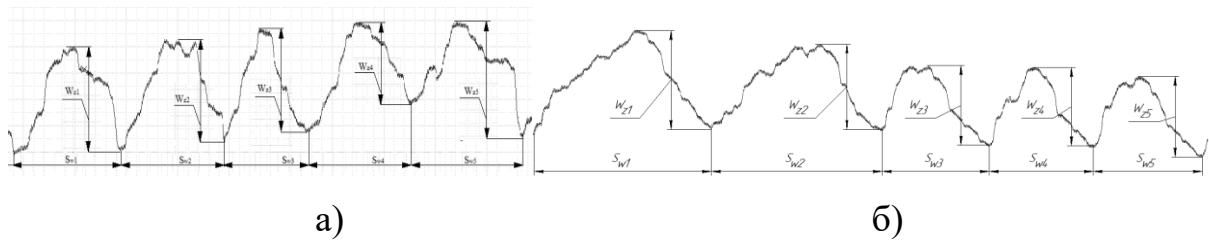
Фрагменти профілограм обробленої поверхні з алюмінію (а) та чавуну (б) після зустрічного кінцевого фрезерування з автоколиваннями
